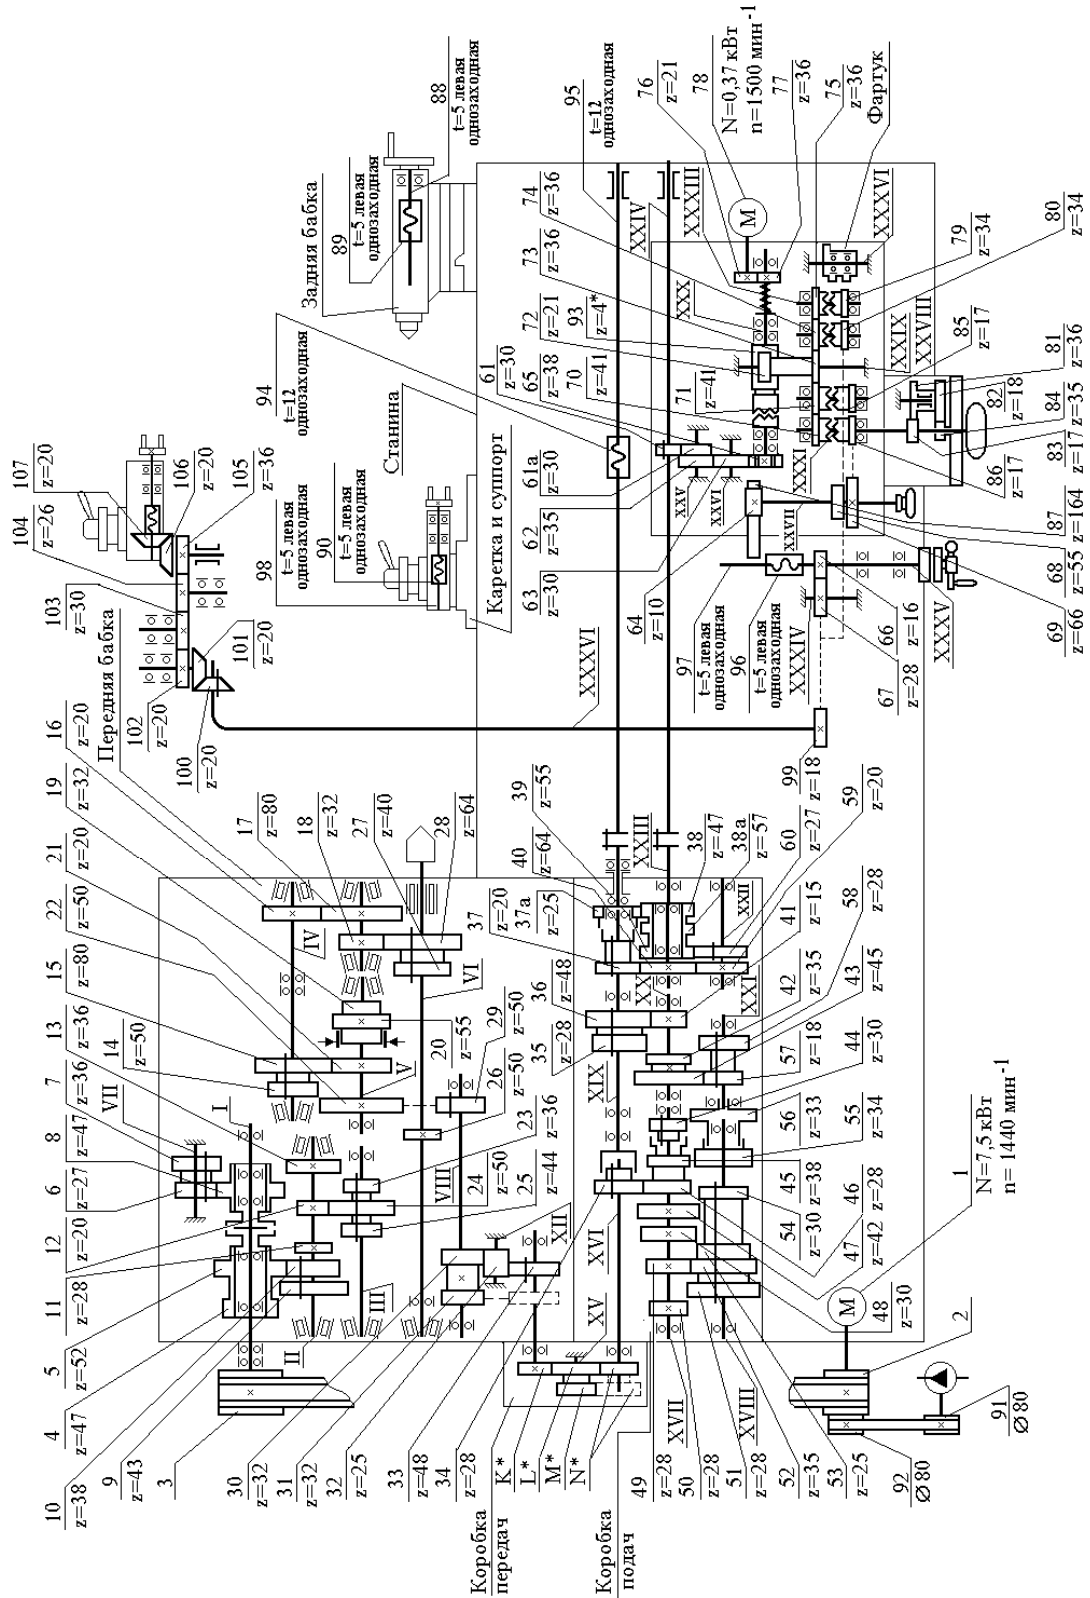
Кинематическая схема станка 16В20А, 1В62ГА, 1В625М с механическим приводом верхнего суппорта
